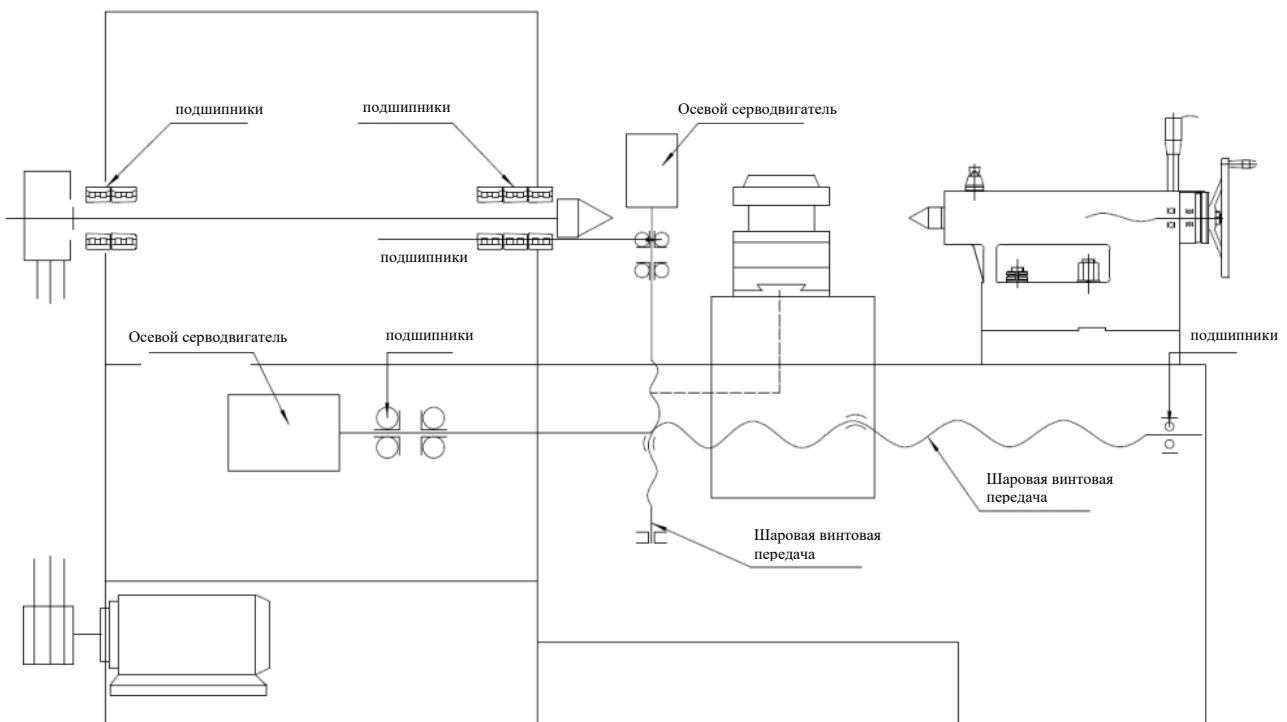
Система приводов для токарного станка с ЧПУ модели СК6140А
